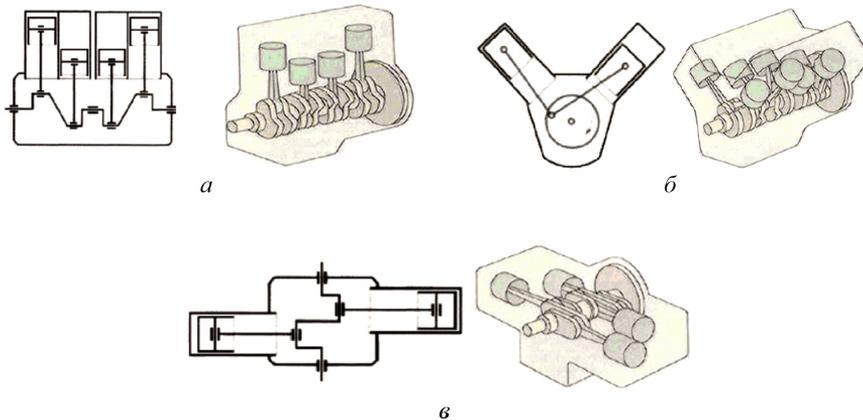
Типы автомобильных двигателей: *а* – рядный четырехцилиндровый двигатель; *б* – V-образный двигатель; *в* – оппозитный двигатель
